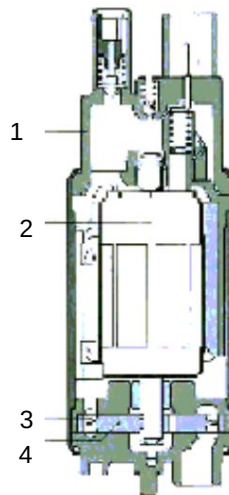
Vista in sezione trasversale della pompa elettrica del carburante
